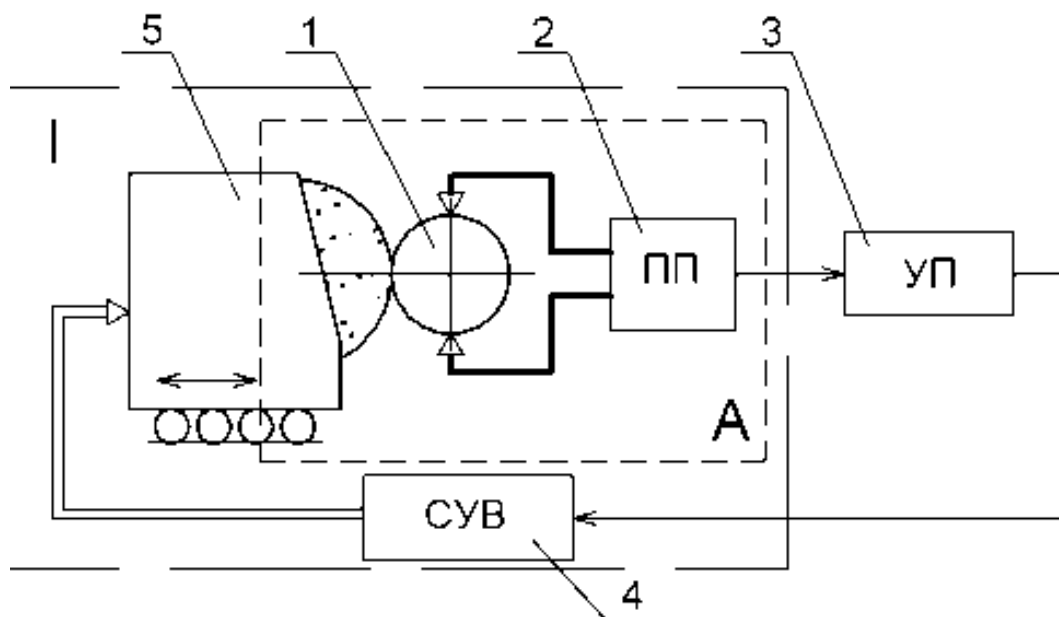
Схема операційного контролю: I – верстат. 1 – деталь, що оброблюється; 2 – первинний вимірювальний перетворювач;
